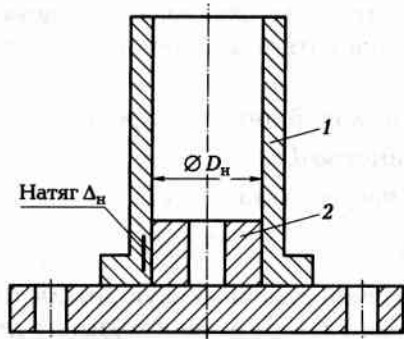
Сборочный чертеж соединения деталей к заданию 7.26
